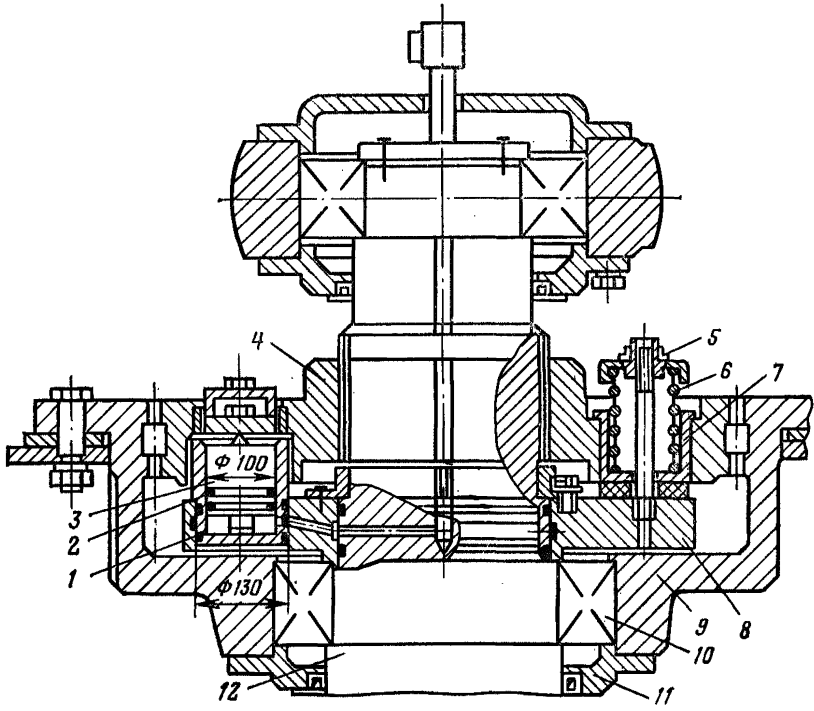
Зубчатый безрычажный механизм перестановки барабанов завода ЛКУ с гидравлическим приводом:
